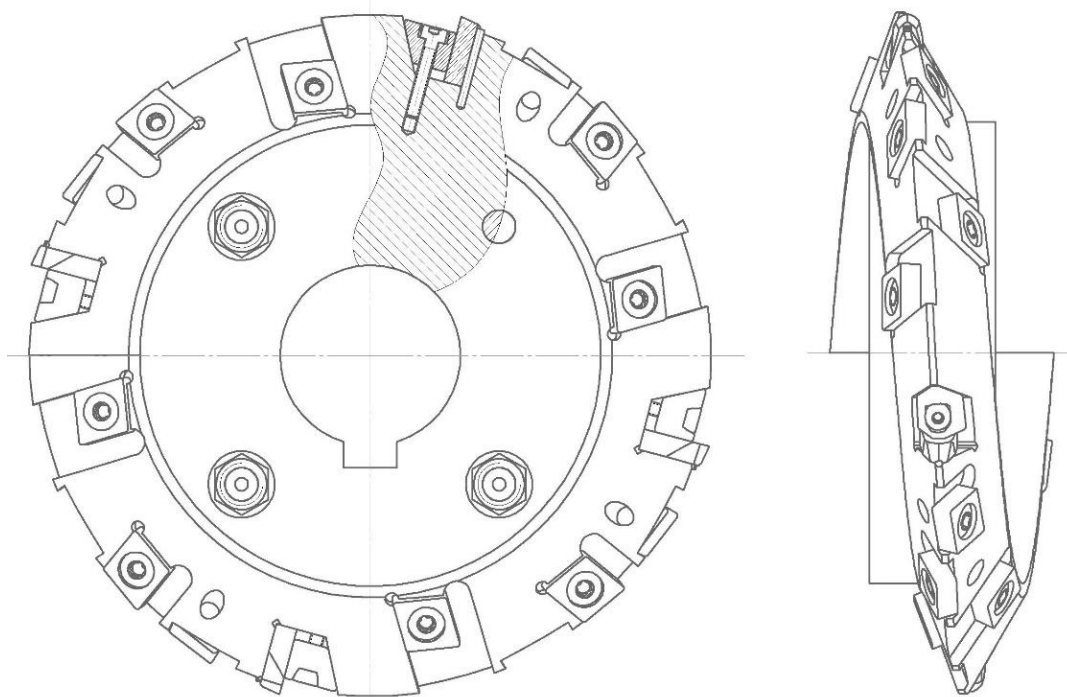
Диск режущего инструмента для формообразования зубчатых колес с нестандартными исходными контурами зацепления
